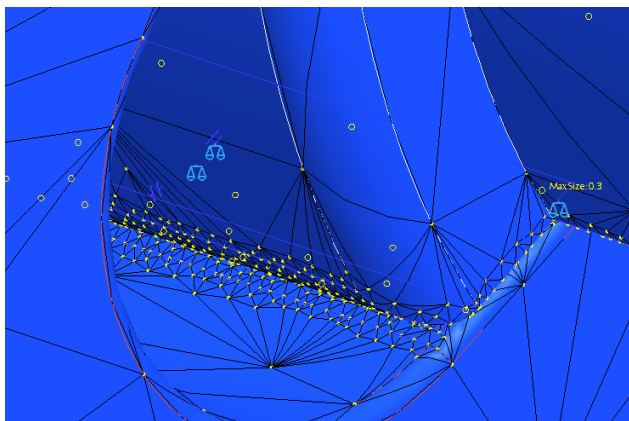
Zhotovený model pro zjištění tuhosti v Pro ENGINEERu - mechanica
